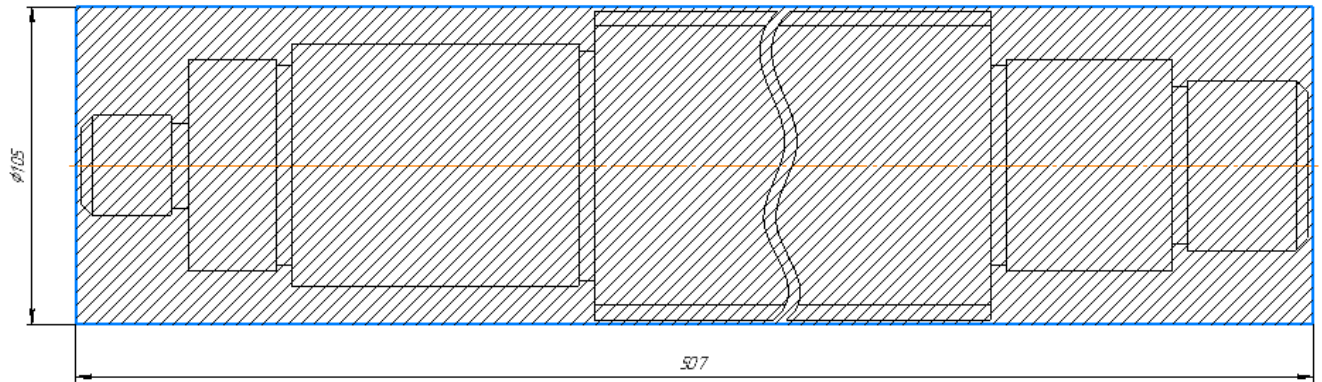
Ескіз заготовки виготовленої з прокату
